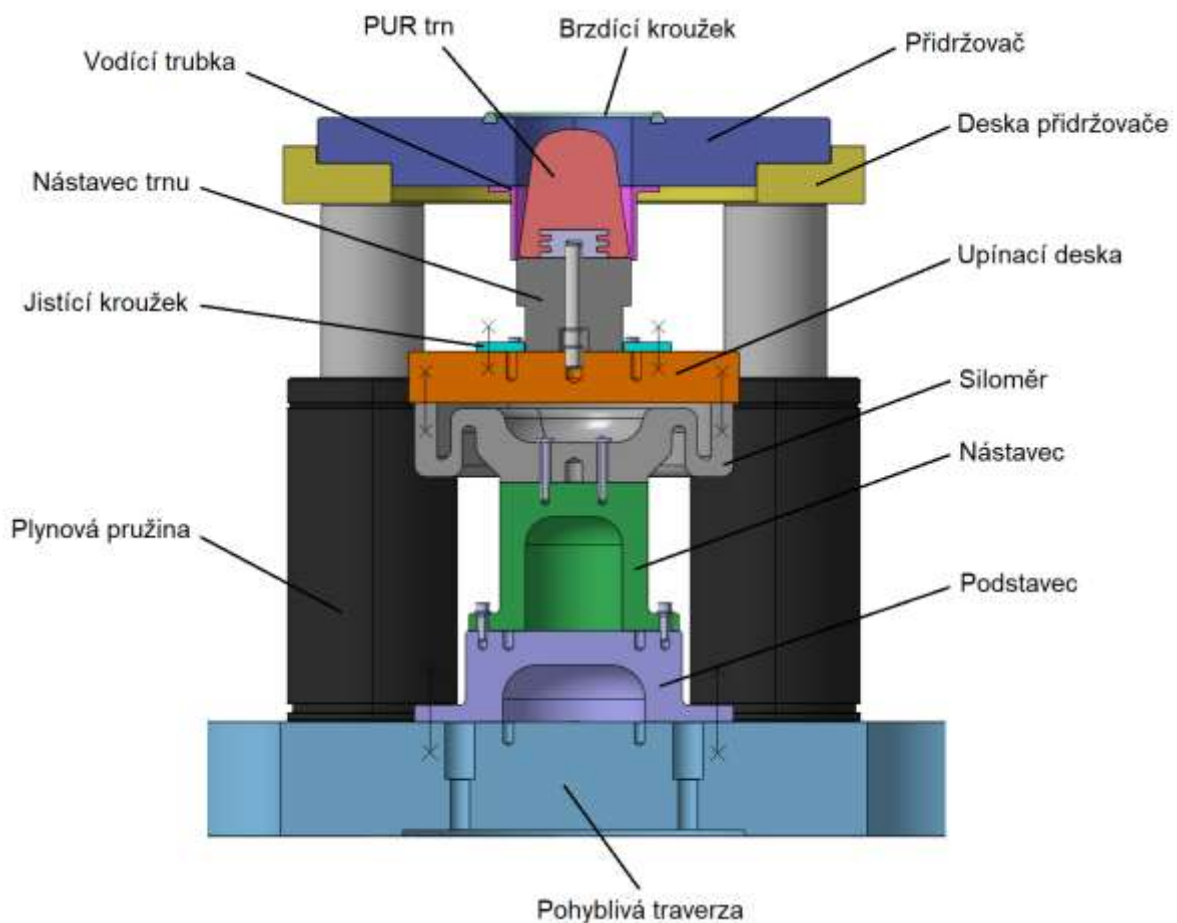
Sestava pro hydraulickou zkoušku bulge
